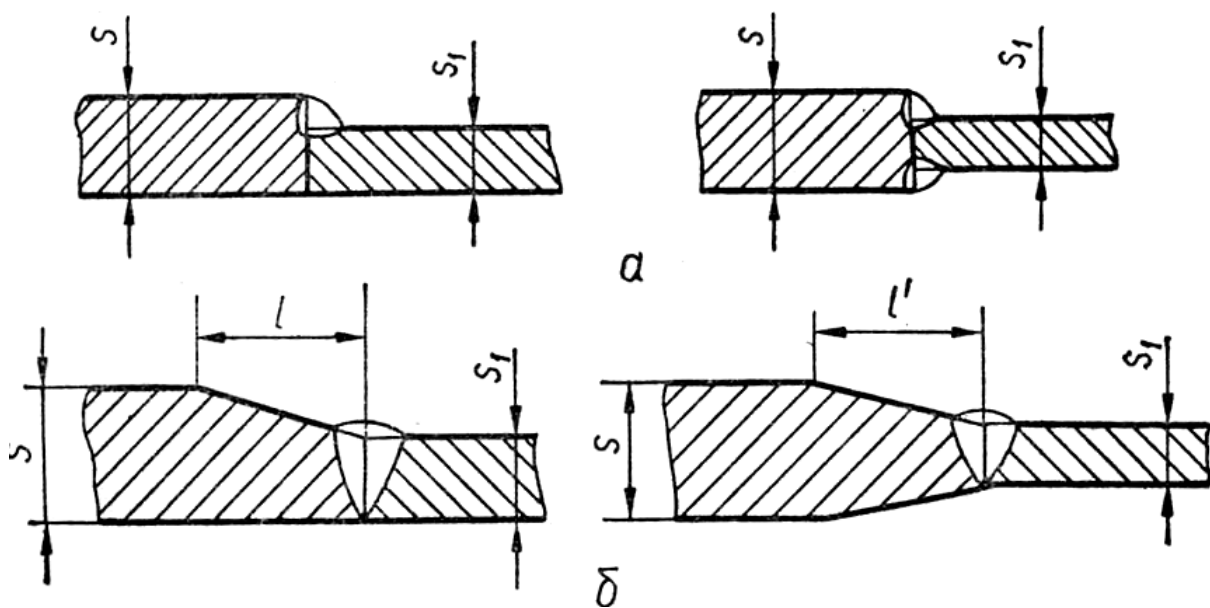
Зварювання вихідних заготовок різної товщини:
